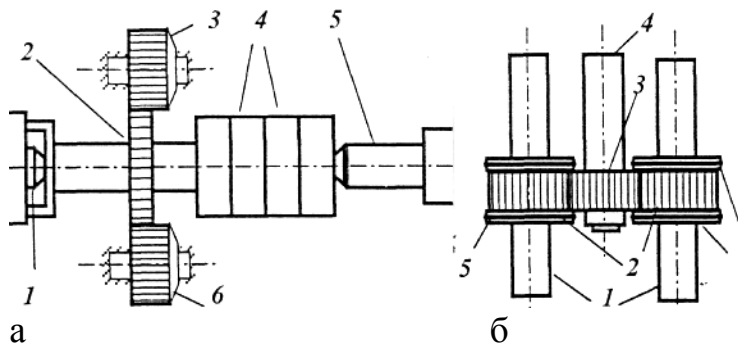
Методы накатывания зубьев цилиндрических зубчатых колес; а - на токарном станке, б - на специальном стенде.
